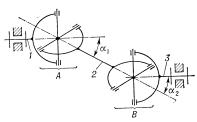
Схема двойного шарнира Гука: 1 — ведущий вал; 2 — промежуточный вал; 3 — ведомый вал; A, B — универсальные шарниры.
